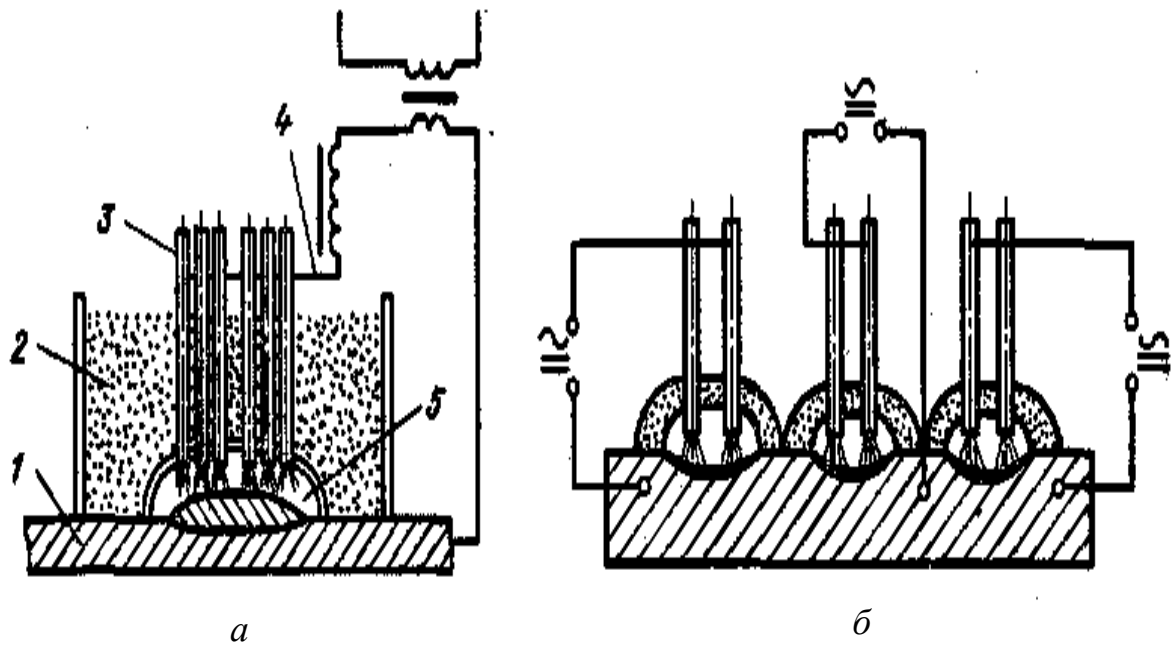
Схема багатоелектродного під флюсом (а) і багатодугового наплавлення (б): 1 — основний метал; 2 — флюс; 3 — дроти
